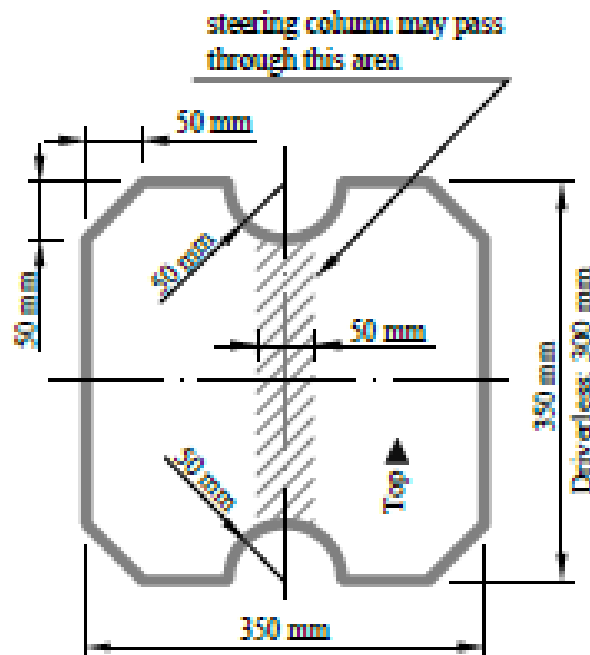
Plantilla de sección transversal de la cabina del piloto. [1]
